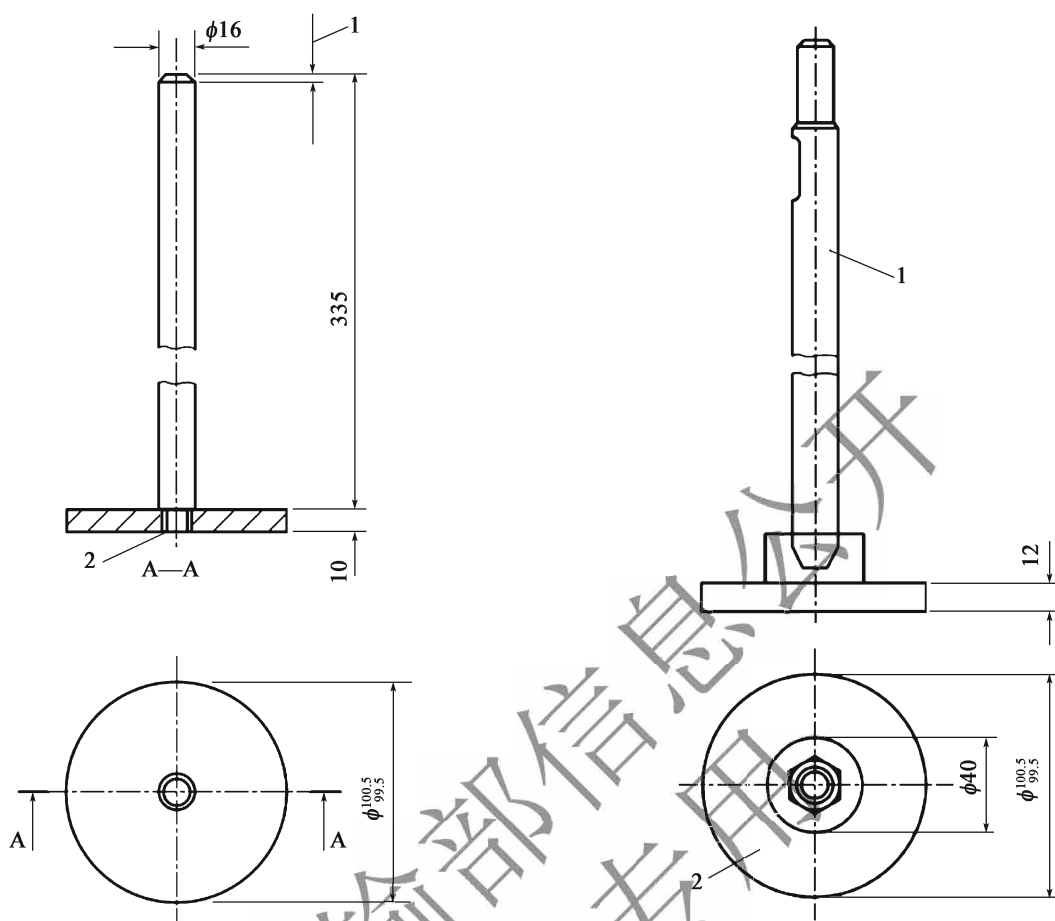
手持式夯锤示意图 (尺寸单位: mm)
